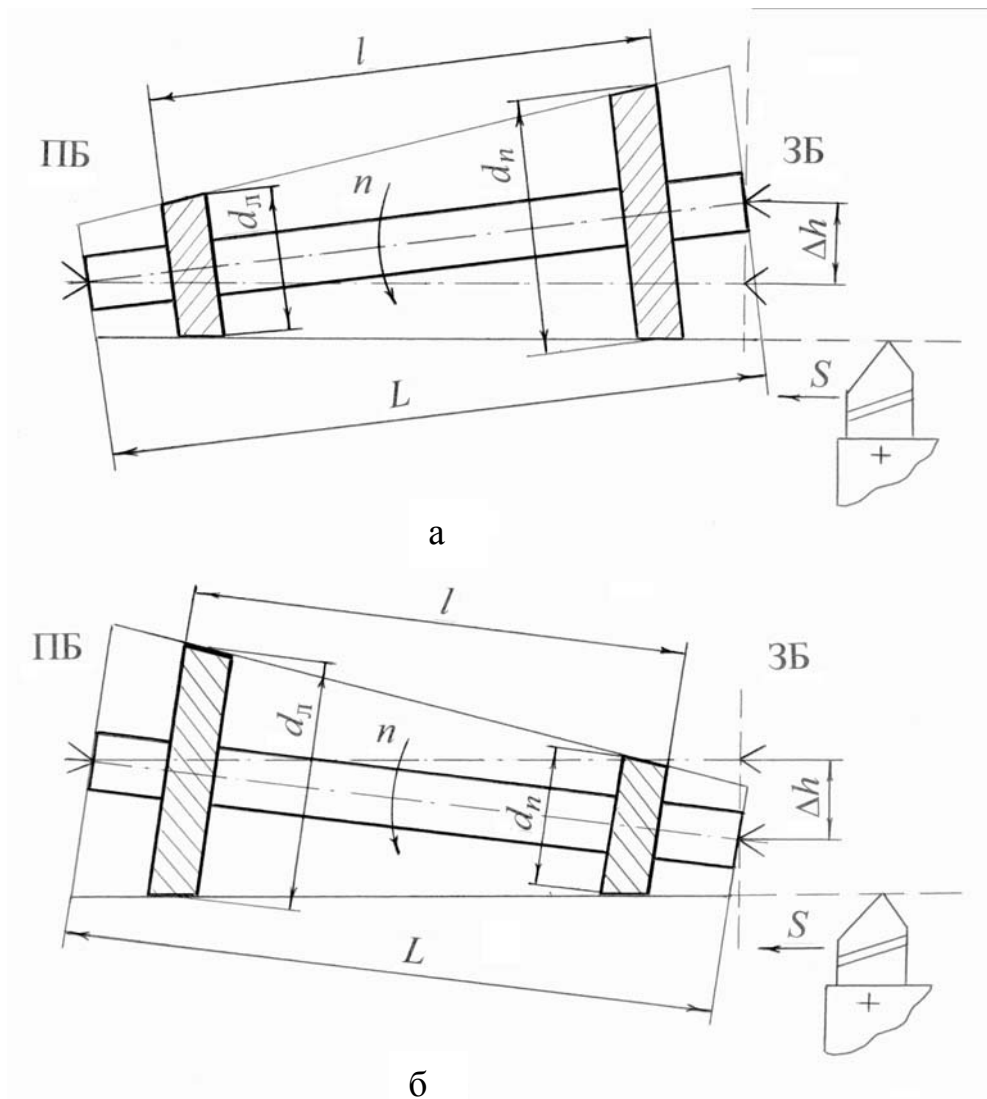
Схема обработки заготовки на токарно-винторезном станке (вид сверху) при смещении задней бабки от (а) и на (б) рабочего: ПБ, ЗБ - передняя и задняя бабки станка (обрабатываемые участки заготовки заштрихованы).
